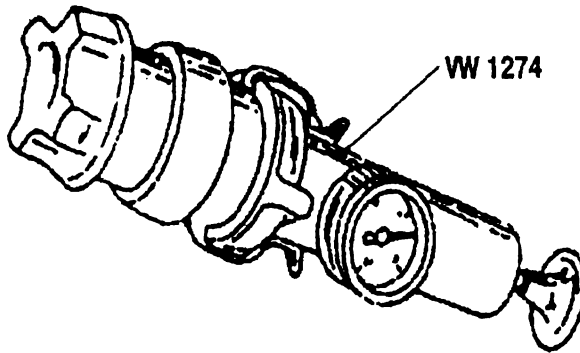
Специальный вакуумный насос для проверки крышки радиатора
